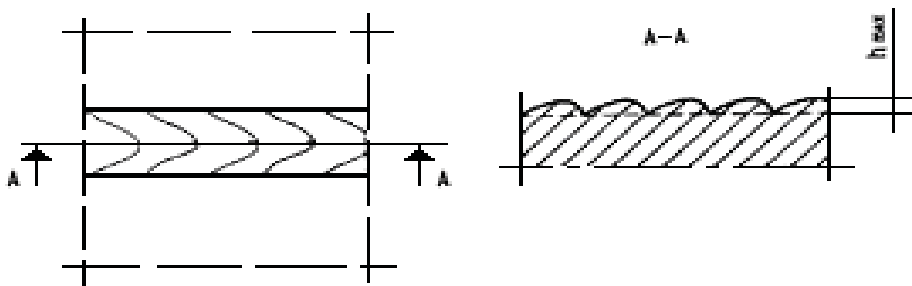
Схематичное изображение чешуйчатости сварного шва
